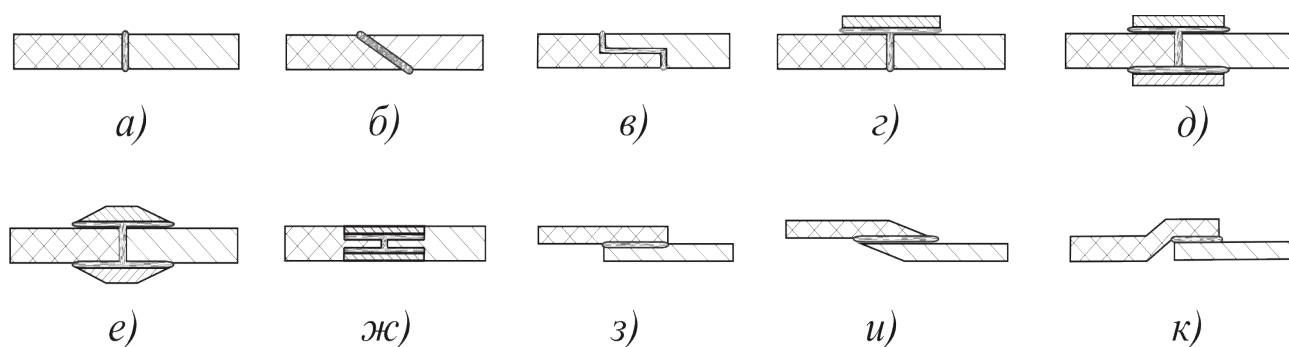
Некоторые виды клеевых соединений: а) стыковое; б) усовое; в) полушиповое; г) стыковое с накладкой; д) стыковое с двумя накладками; е) стыковое со скошенными накладками; ж) стыковое с утопленной двойной накладкой; з) внахлѣст; и) внахлѣст со скосом; к) внахлѣст с подсечкой
